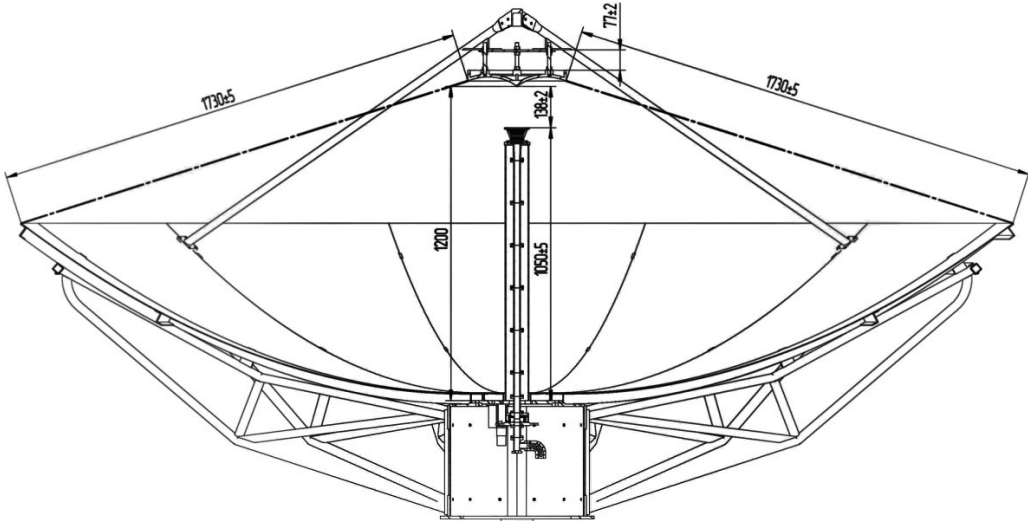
Габаритные и монтажные размеры рефлектора
